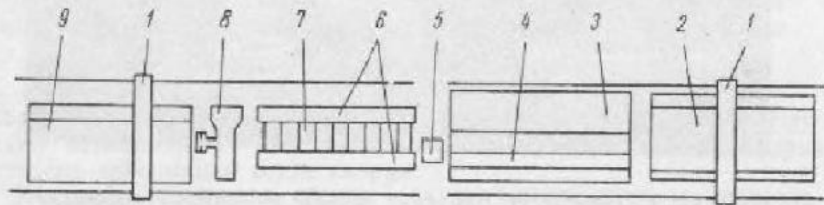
Комплексно-механизированная линия сборки и сварки тавровых балок.
